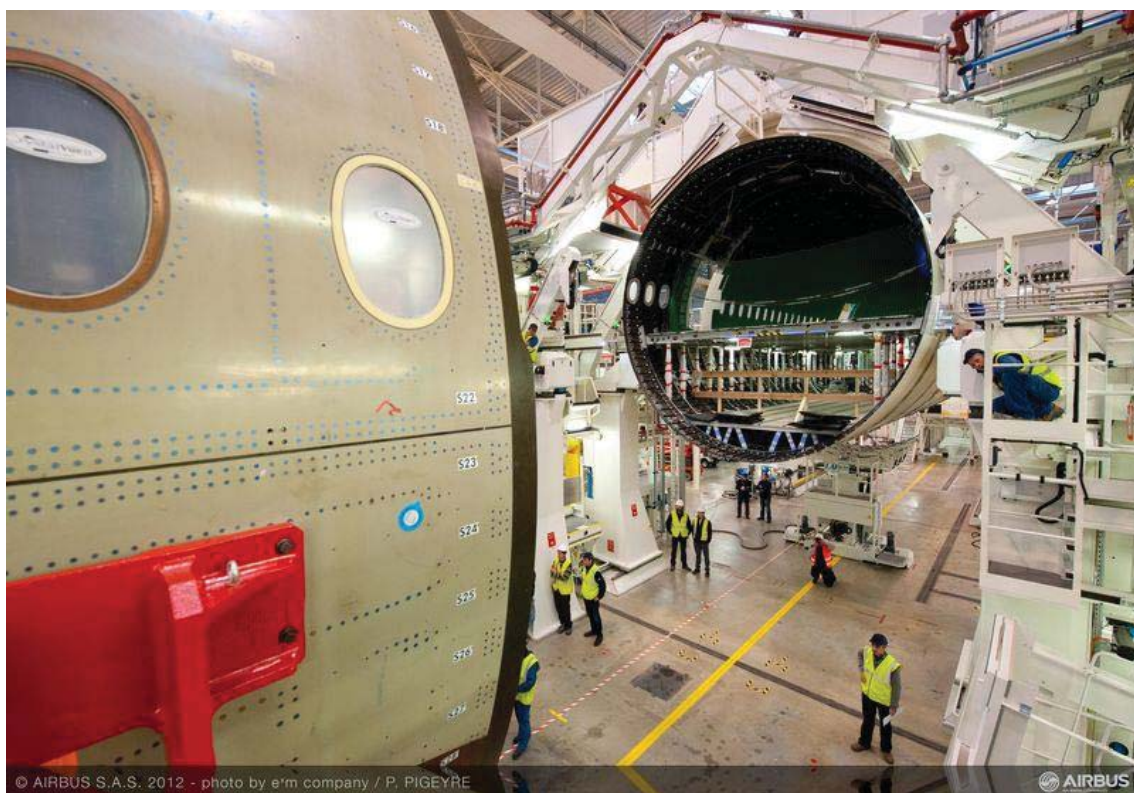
Ensamblaje de subcomponentes para construcción de fuselajes: pueden observarse las líneas de remaches utilizados para la construcción de los subcomponentes.
